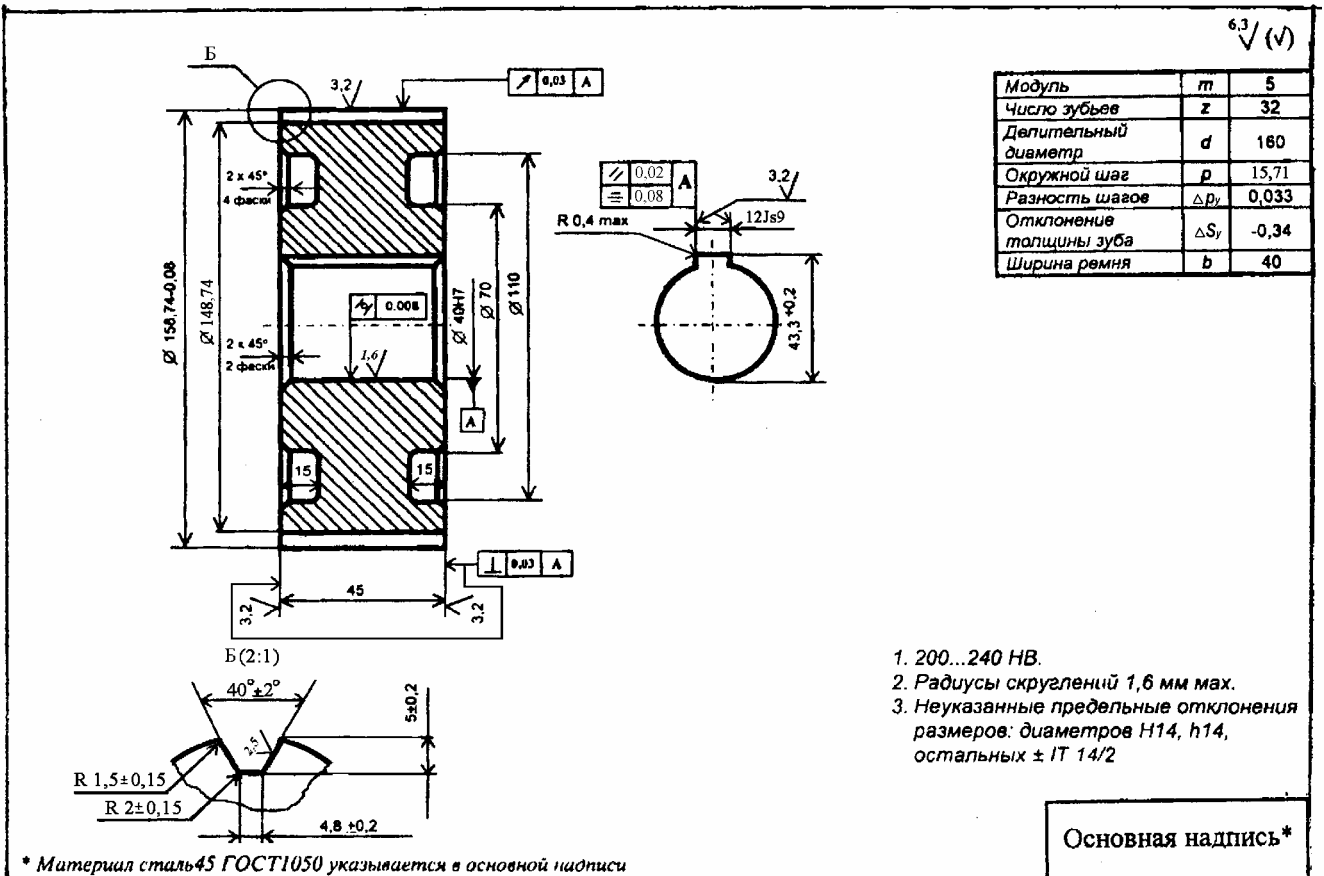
Рабочий чертеж шкива для зубчатого ремня
